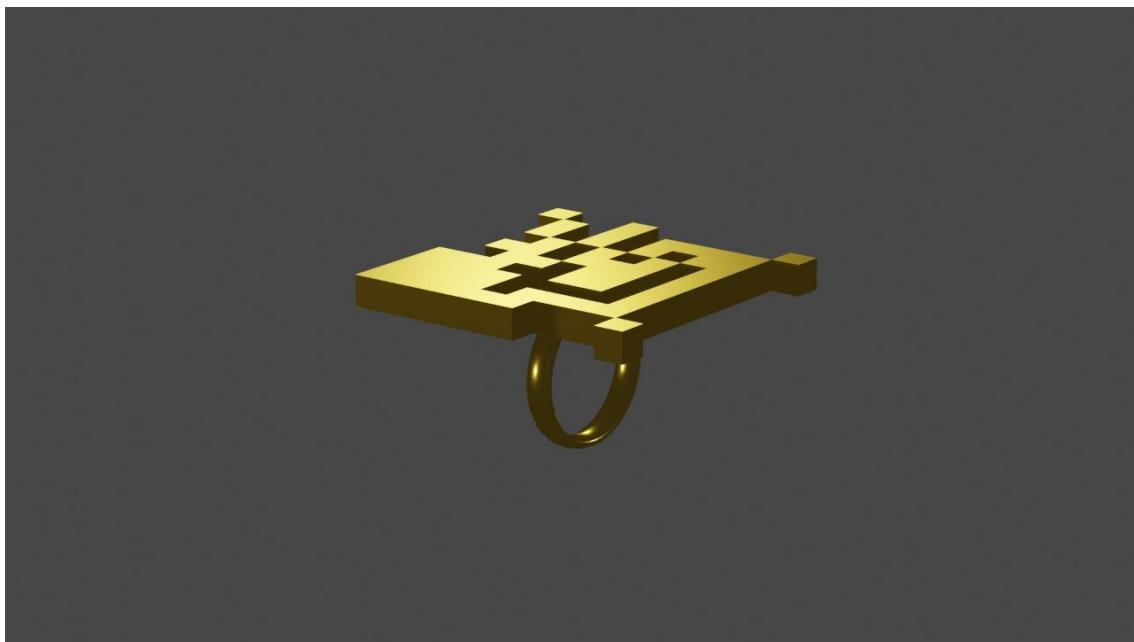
Uma solução para o problema das “ilhas” de cubinhos seria colocar um plano sob eles.
